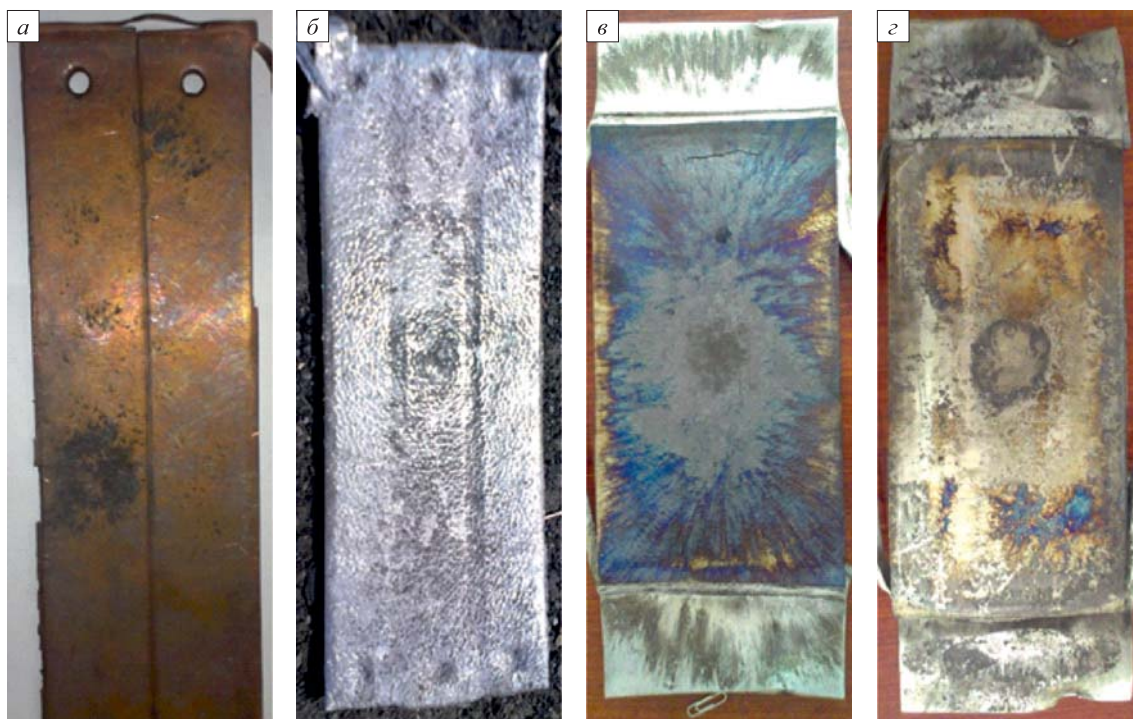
Композиции, полученные сваркой взрывом:
